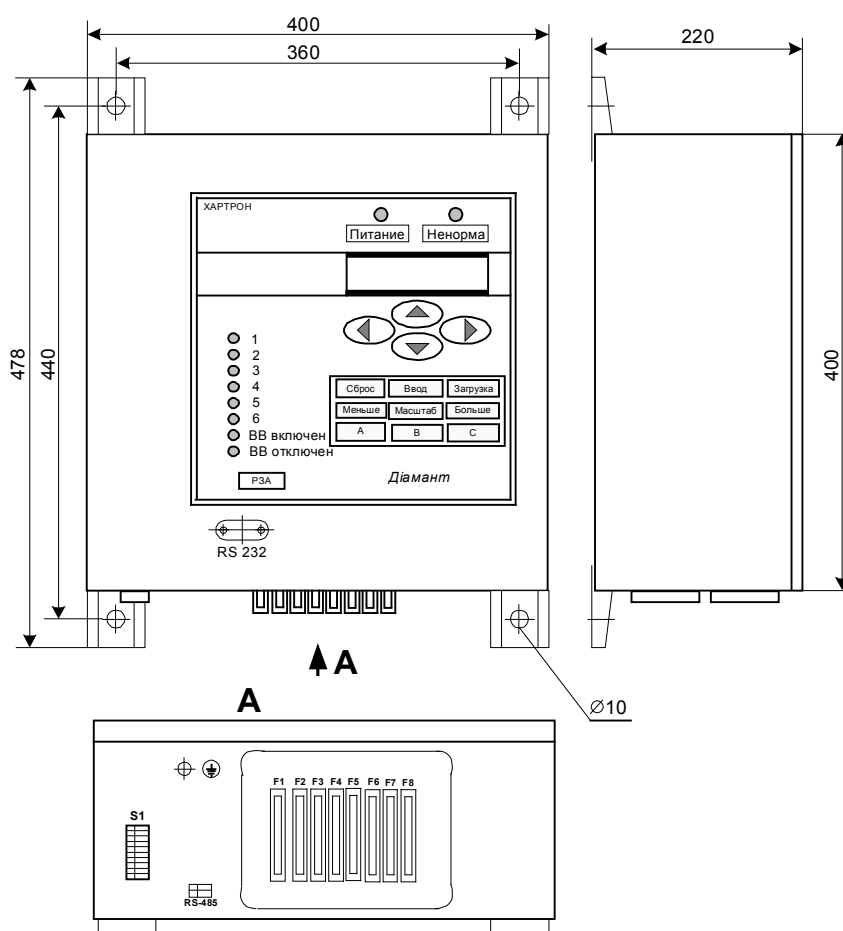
Габаритно – установочный чертеж ПМ РЗА
